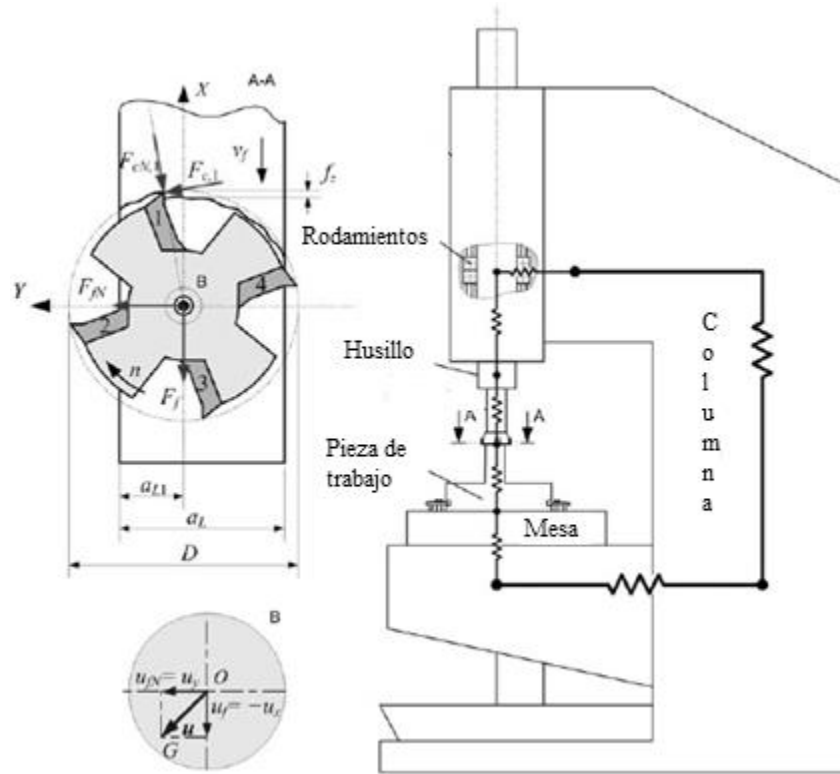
Geometría de fresado frontal y dinámica de una fresadora.[25]
